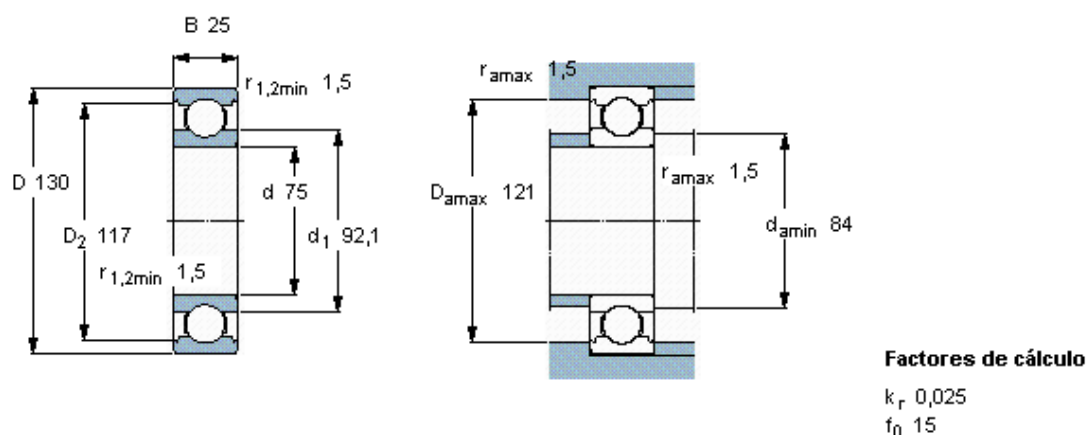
Dimensiones del Rodamiento SKF 6215.
